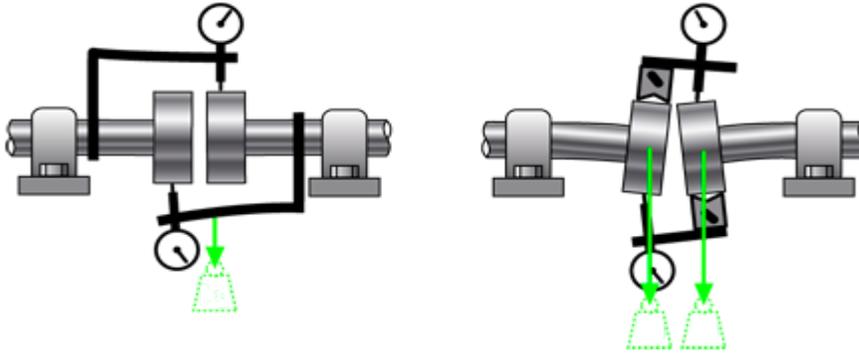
DES ALINEAMIENTO AXIAL
